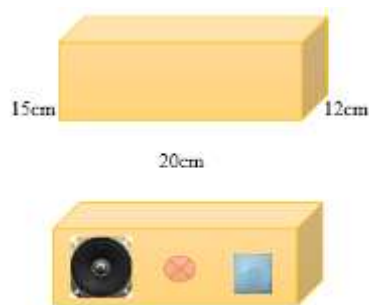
Dimensiones del proyecto con el módulo AD9833
